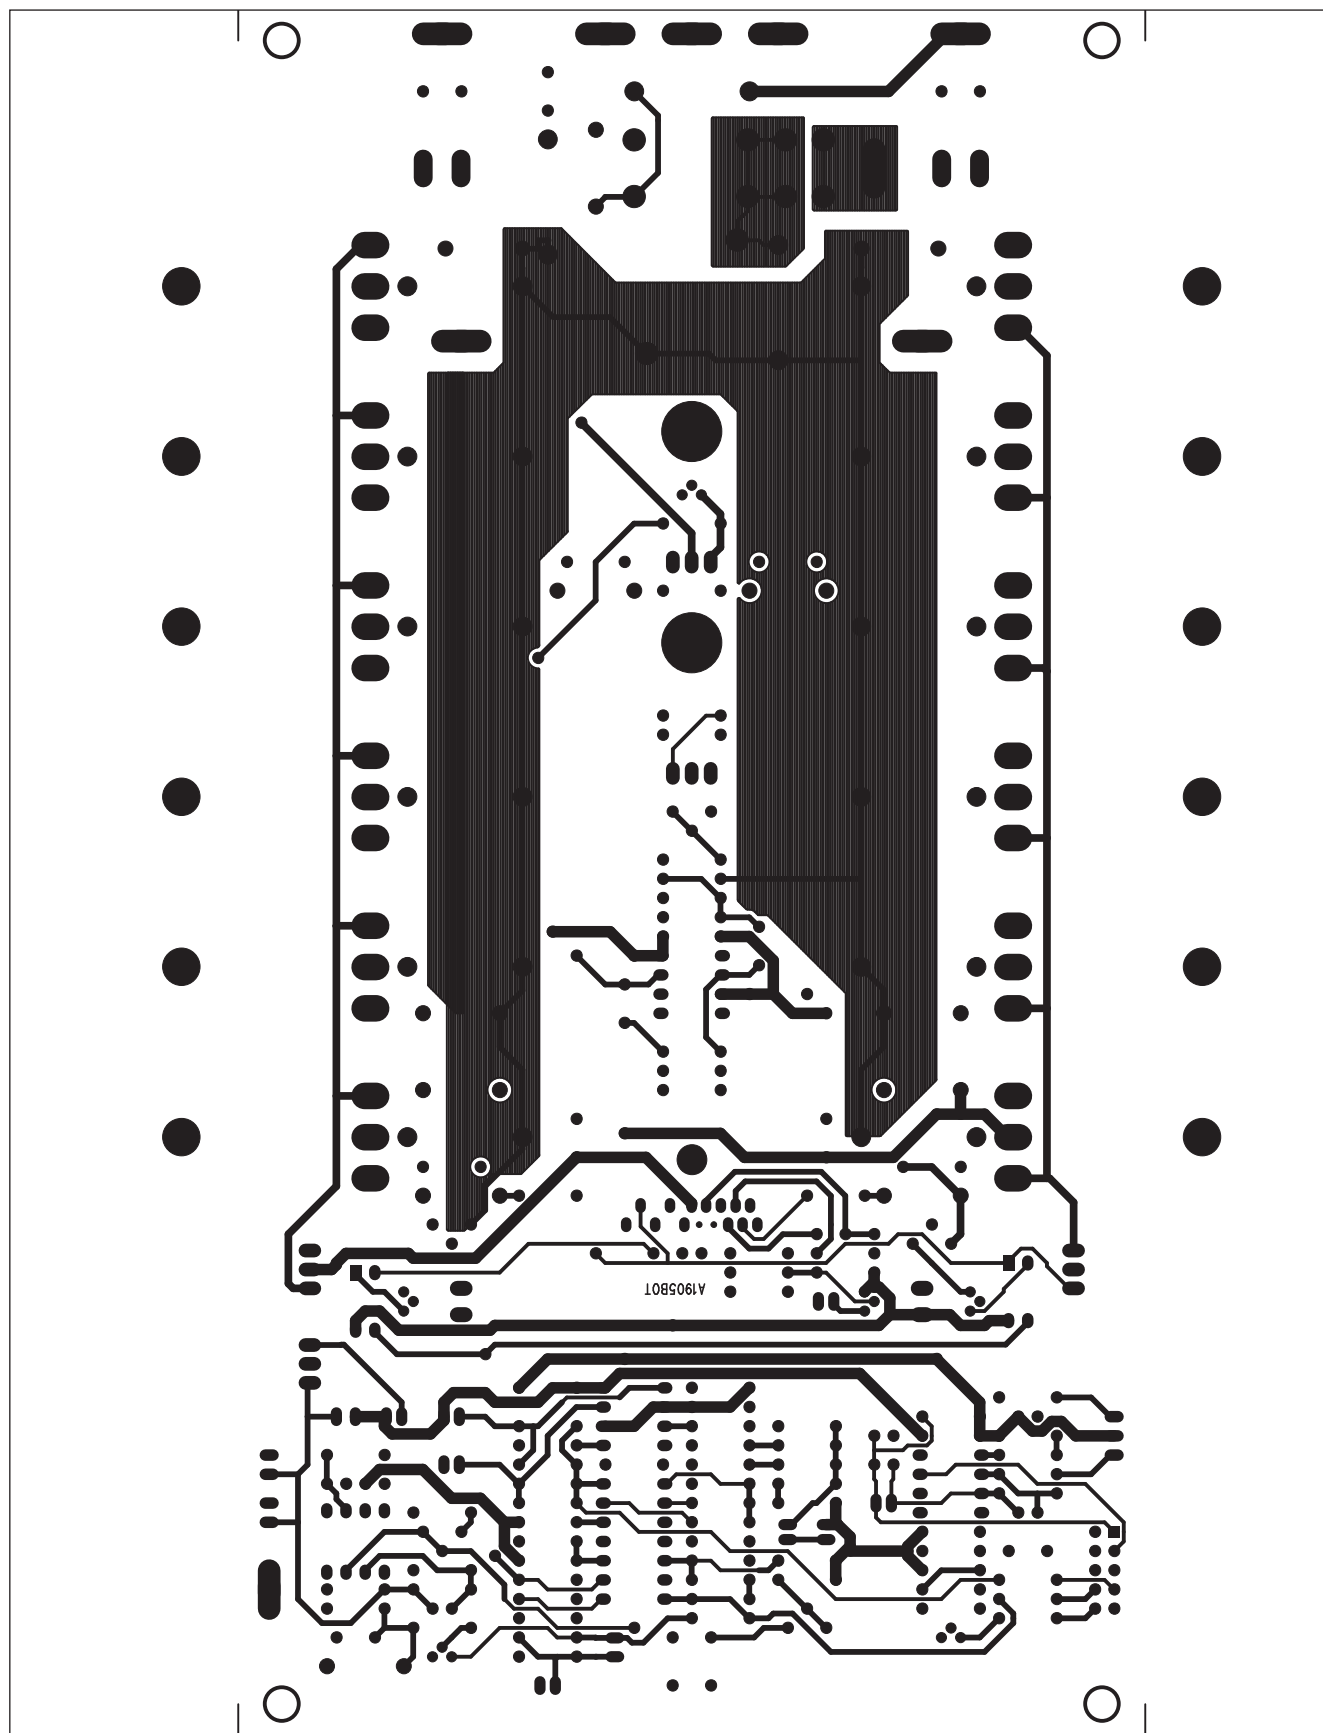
Obrazec desky spojů zesilovače (strana TOP)
